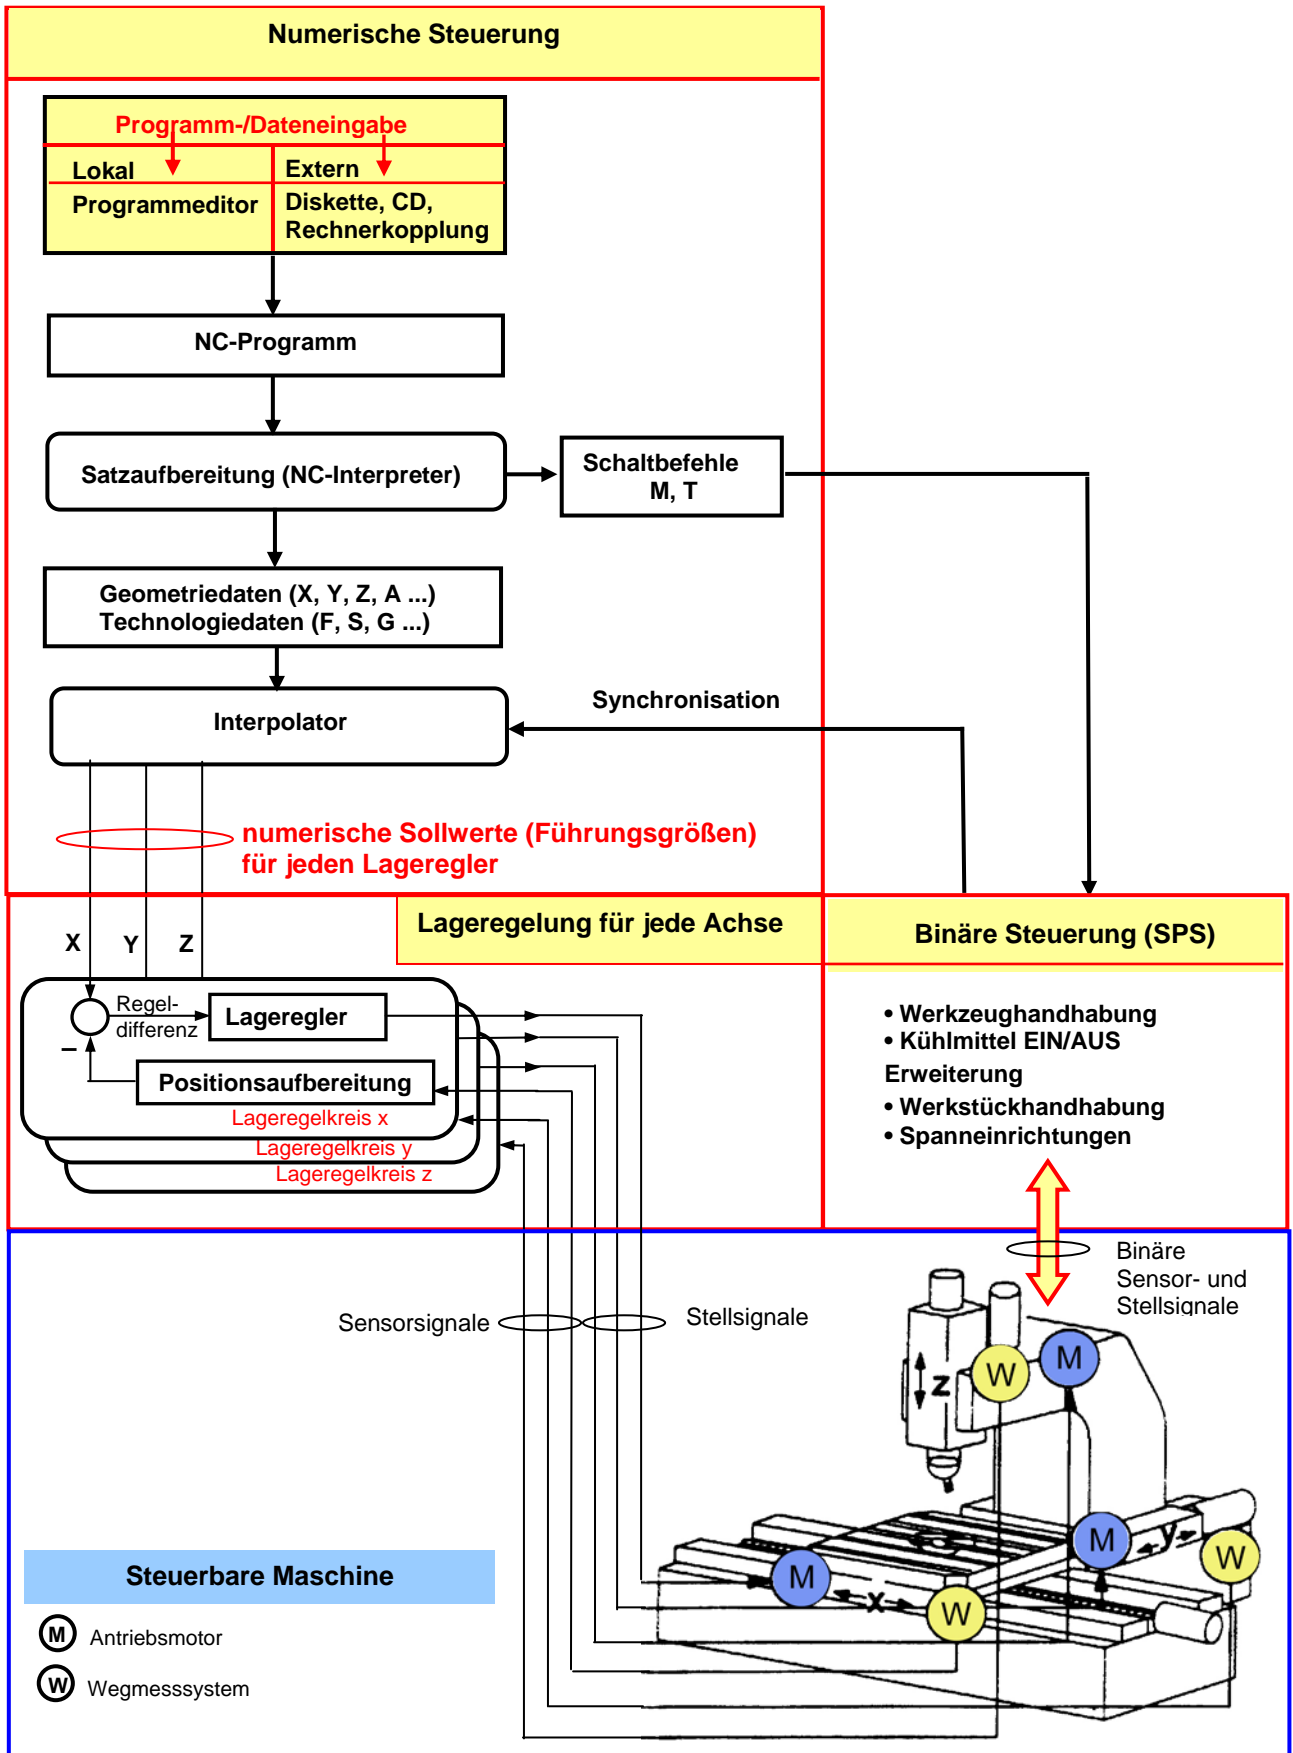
Prinzip der Steuerung einer numerischen Bearbeitungsmaschine
